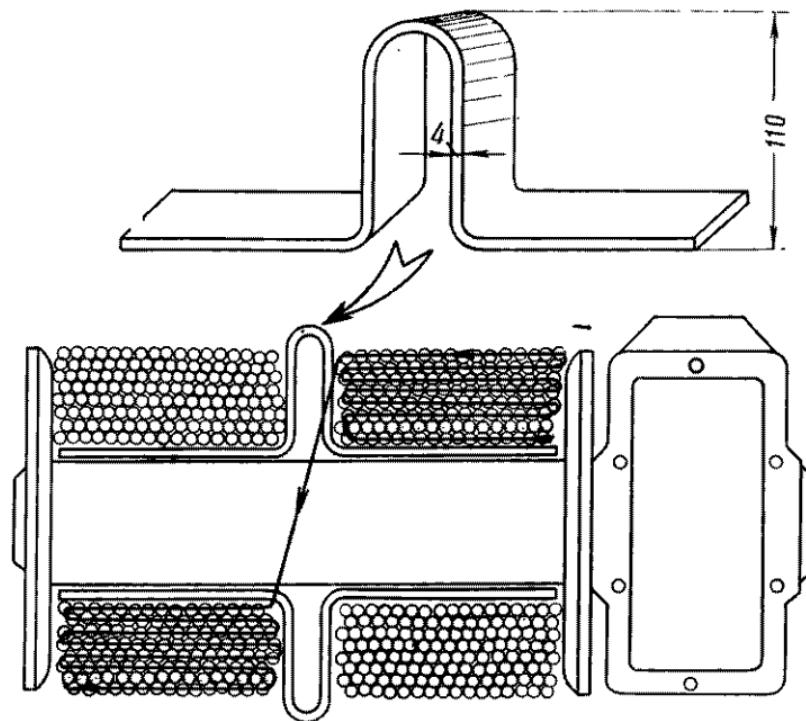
Общий вид приспособления для укладки троса и установки его на барабан лебедки автомобиля ЗИЛ-151А
